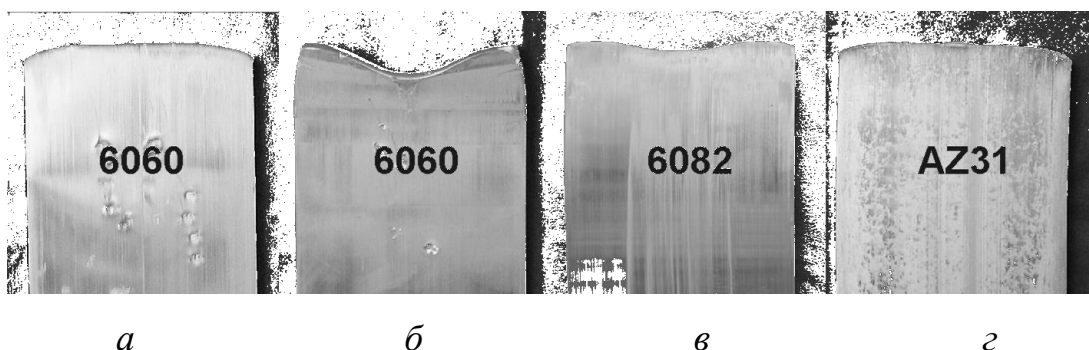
Форма переднього кінця штаб: а - пресування через плоску матрицю; б-г - через форкамерну
